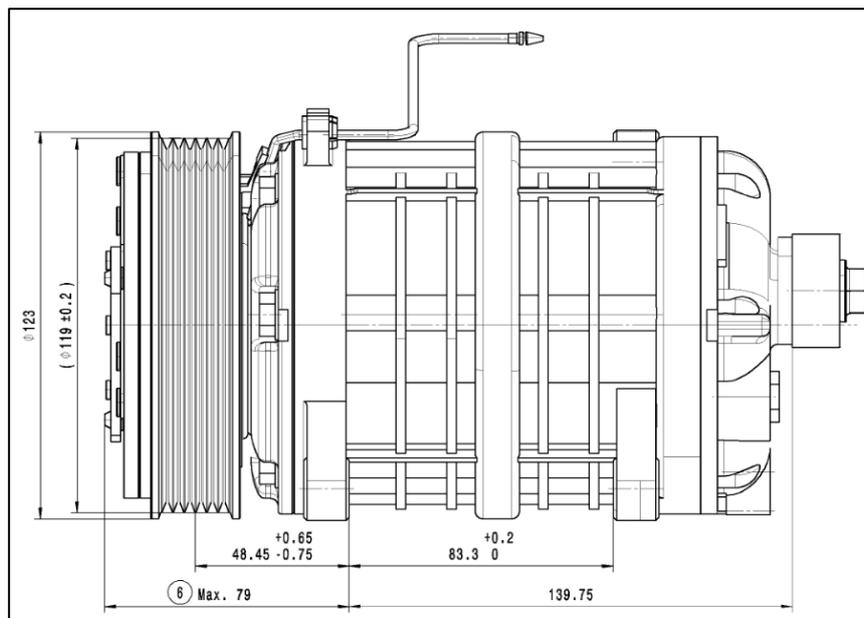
dimensioni compressore (7C0.816.803 D/E), vista laterale
